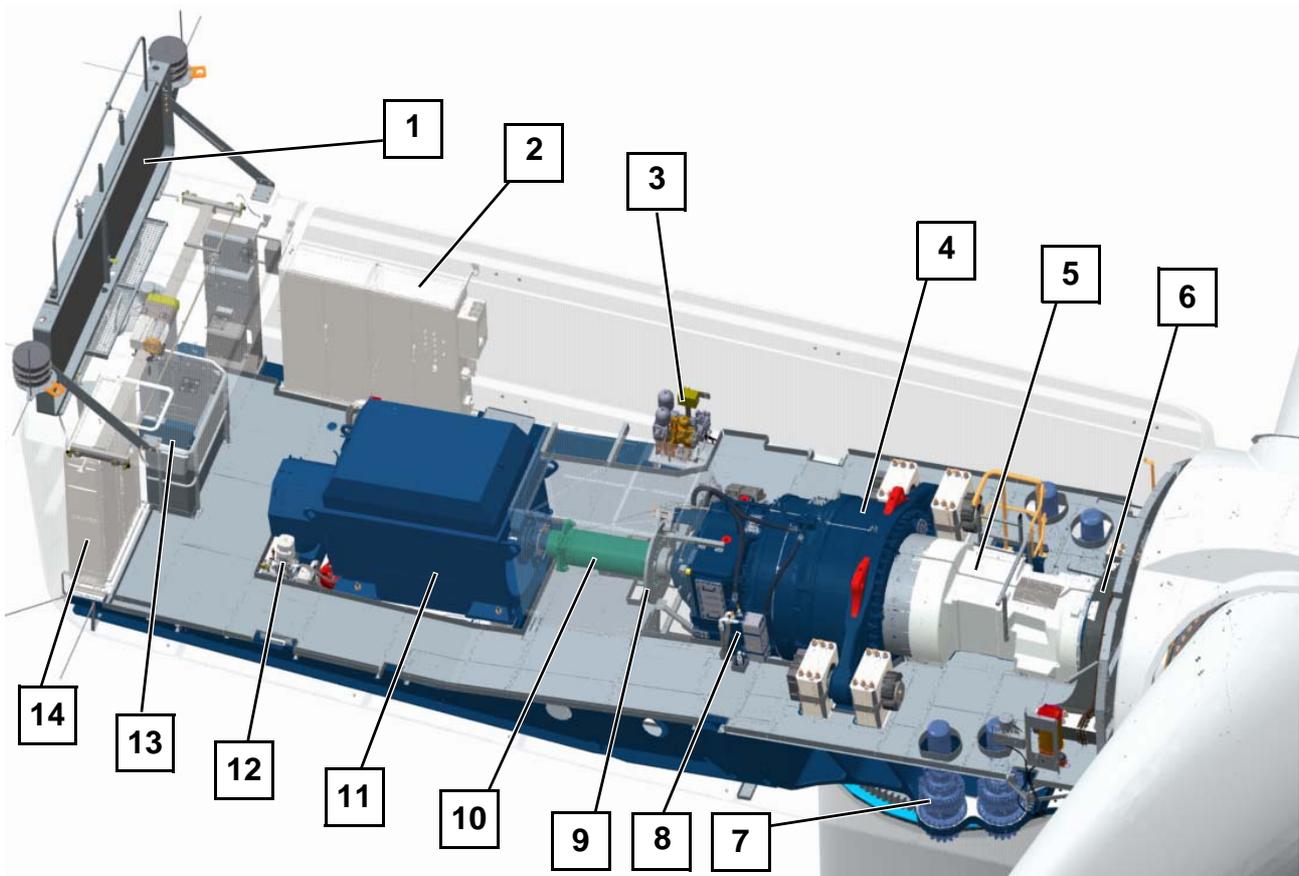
Übersichtszeichnung Maschinenhaus
